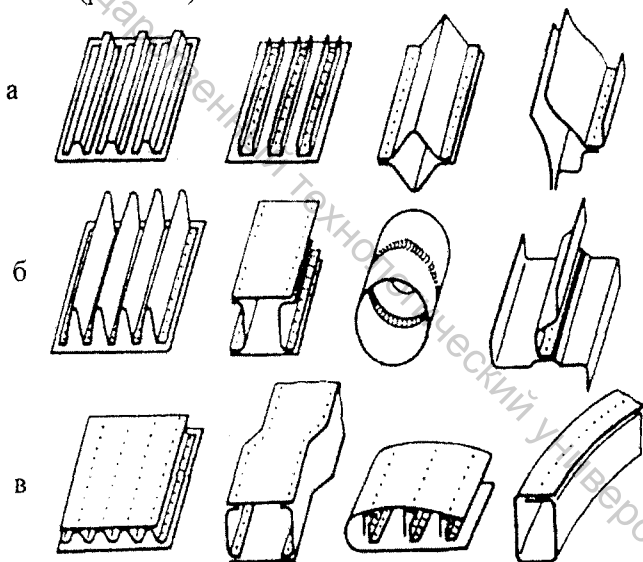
Сварные узлы открытого (а), полузакрытого (б) и закрытого (в) типов
